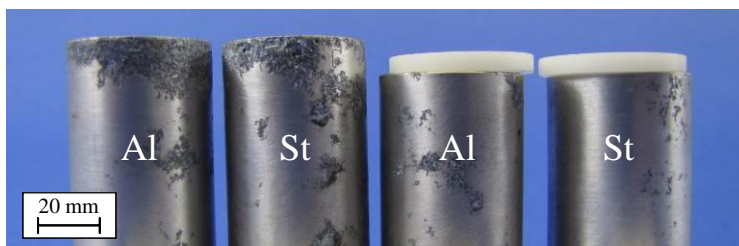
Mg-Zylinder nach Klimawechseltest mit Al- und St-Schrauben
